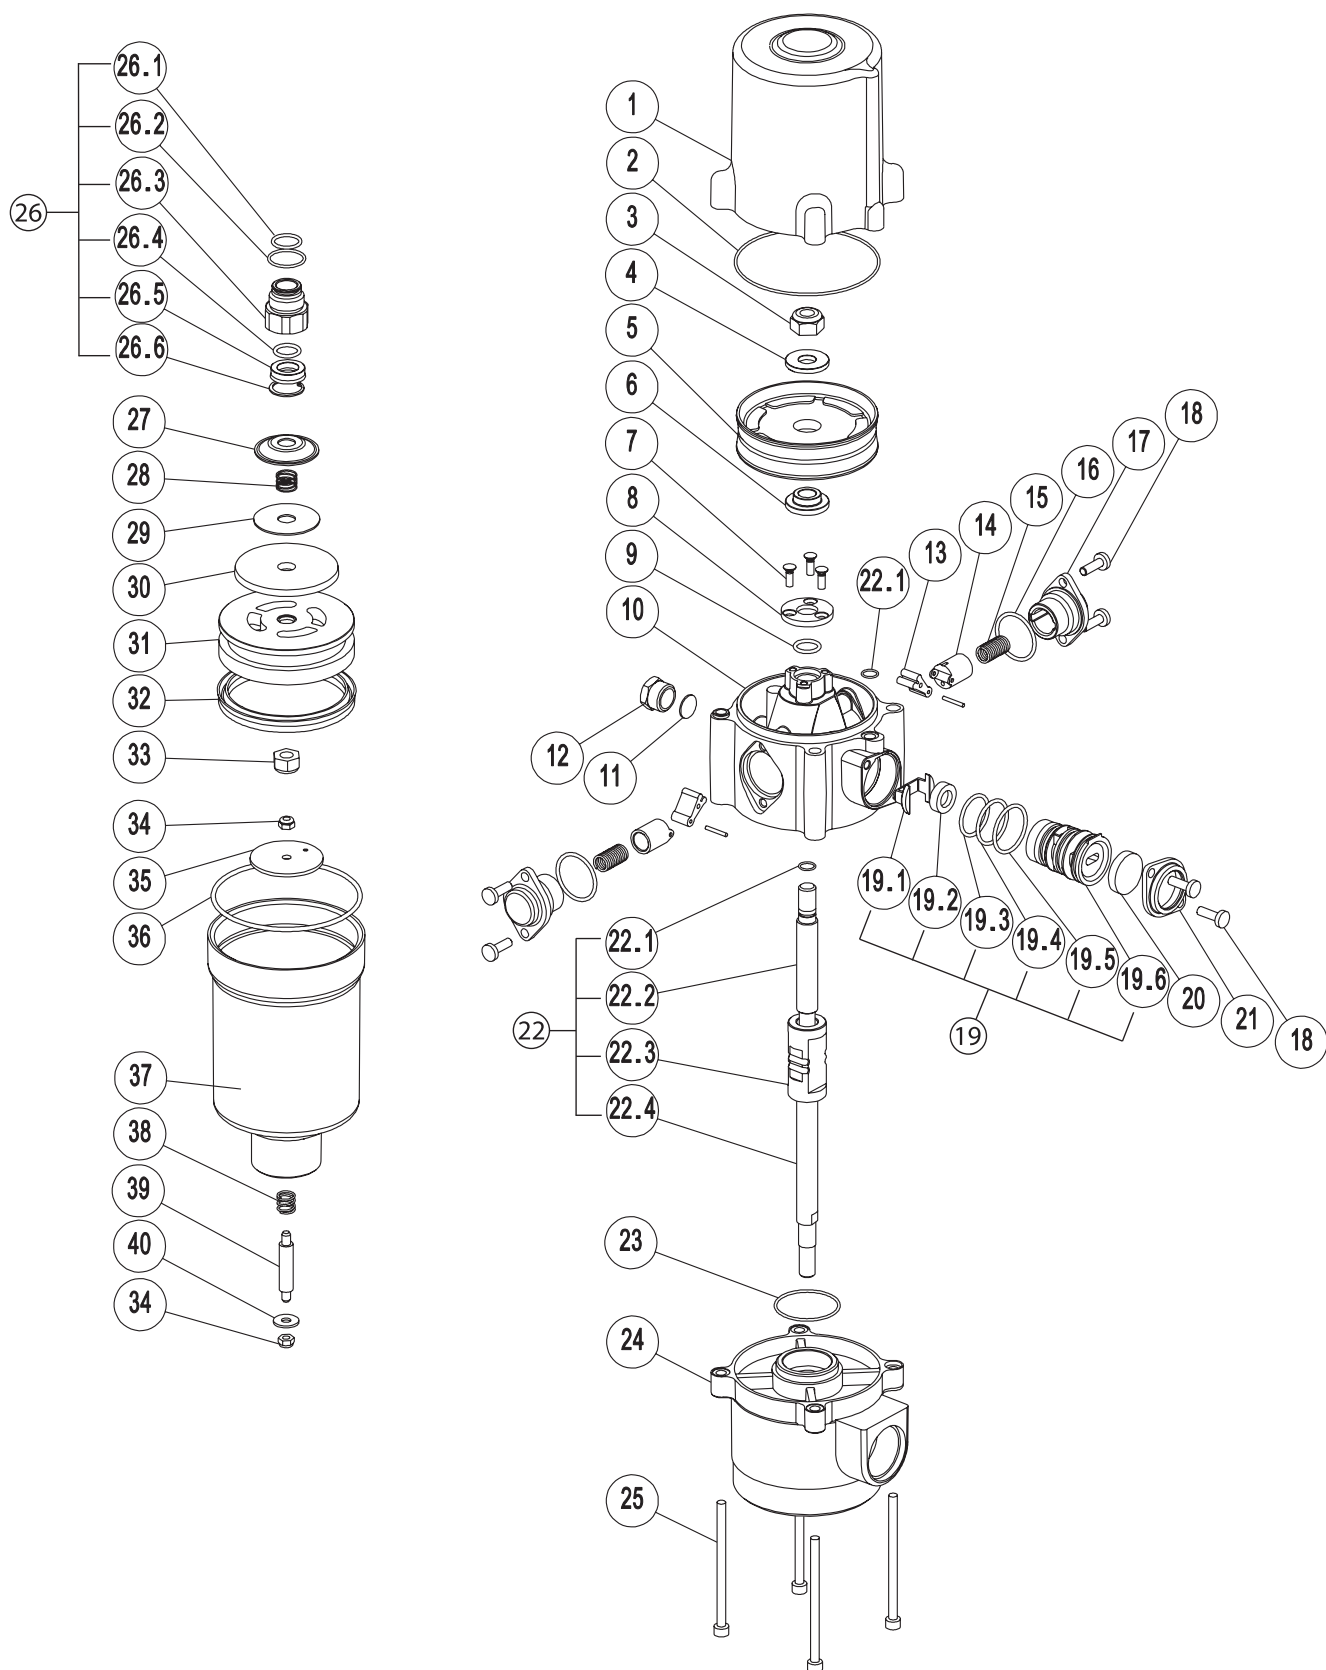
Vue éclatée de la Pompe pneumatique huile
